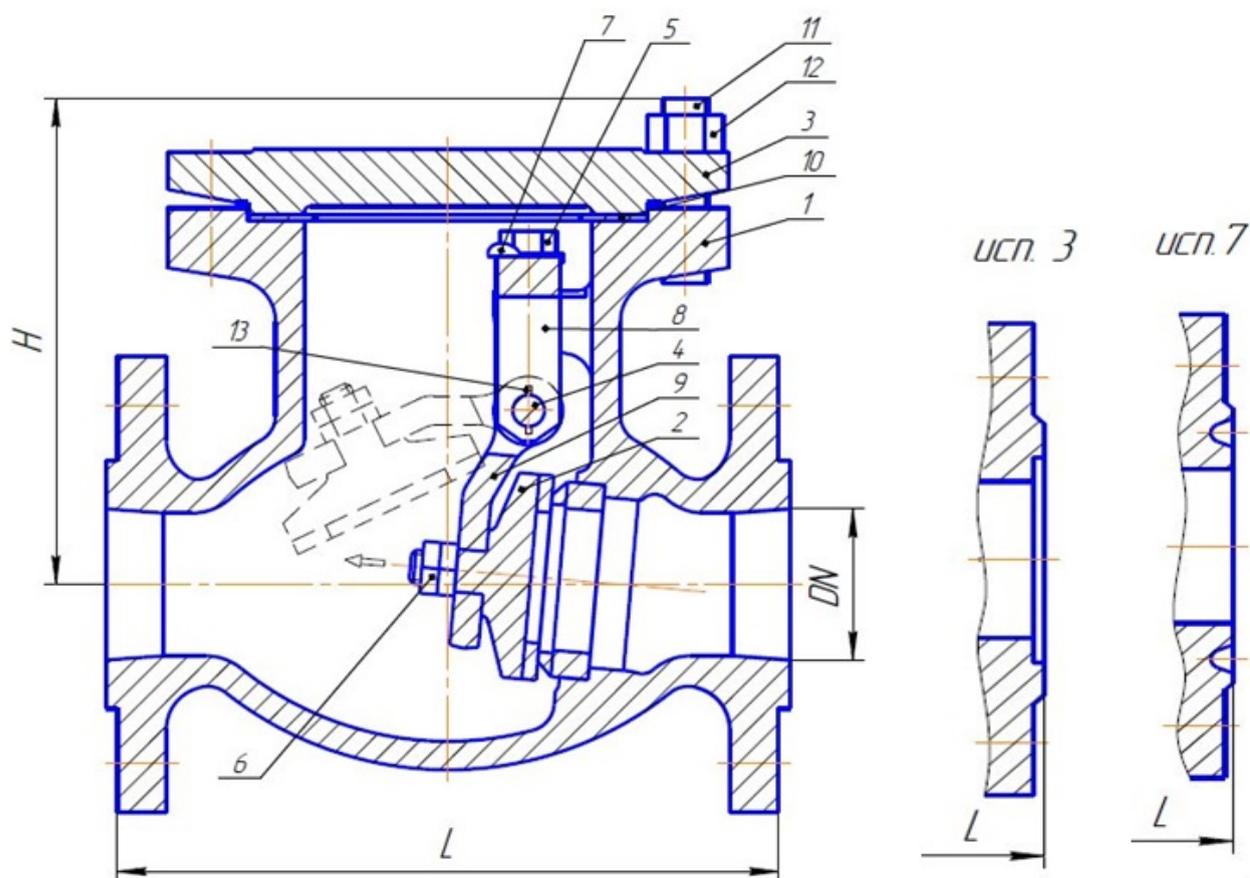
Общий вид и устройство клапана обратного поворотного*.
